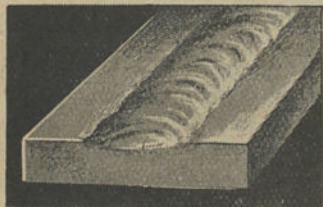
Soldadura insuficientemente carregada.
